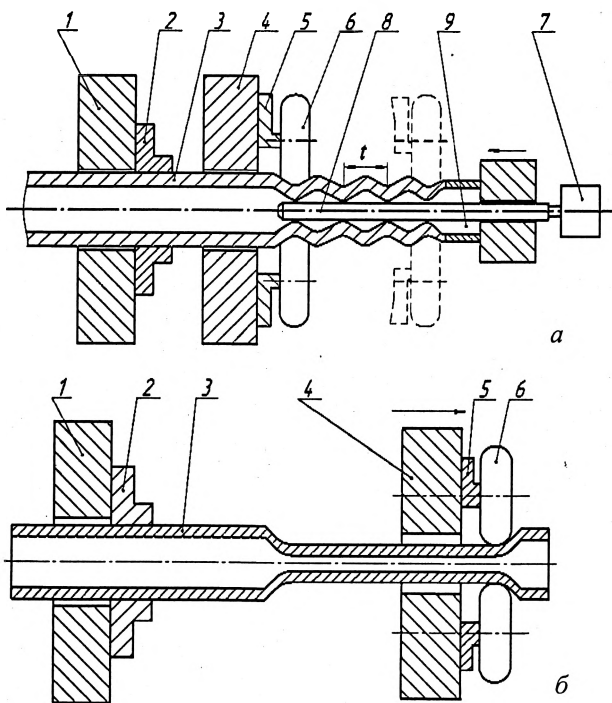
Схема устройства для изготовления полуосевых рукавов
